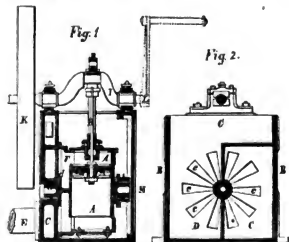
zeigt den Durchschnitt dieser Pumpe. Der Pumpenschleifer A oscillirt um die Zapfen a, deren Lagerfassung b innerhalb des Gefäßes B angebracht sind. Dieses Gefäß ist auf der einen Seite in eine Saugkammer C und eine Stößkammer D zerlegt, wie Fig. 2 zeigt, und die dem Cylindri A zunächst liegende Seitenwand ist mit Canälen c versehen. Gleich gefaltete Canäle d sind in der Seitenwand des Cylinders A ausgeparbt. E ist ein Saugrohr, F der Stößkammer, G der Pumpenfelben, H die Kurbelstange, I die gefräßte Weile, K das Schwungrad, L eine Handkurbel, durch welche die Pumpe in Betrieb gesetzt wird.
